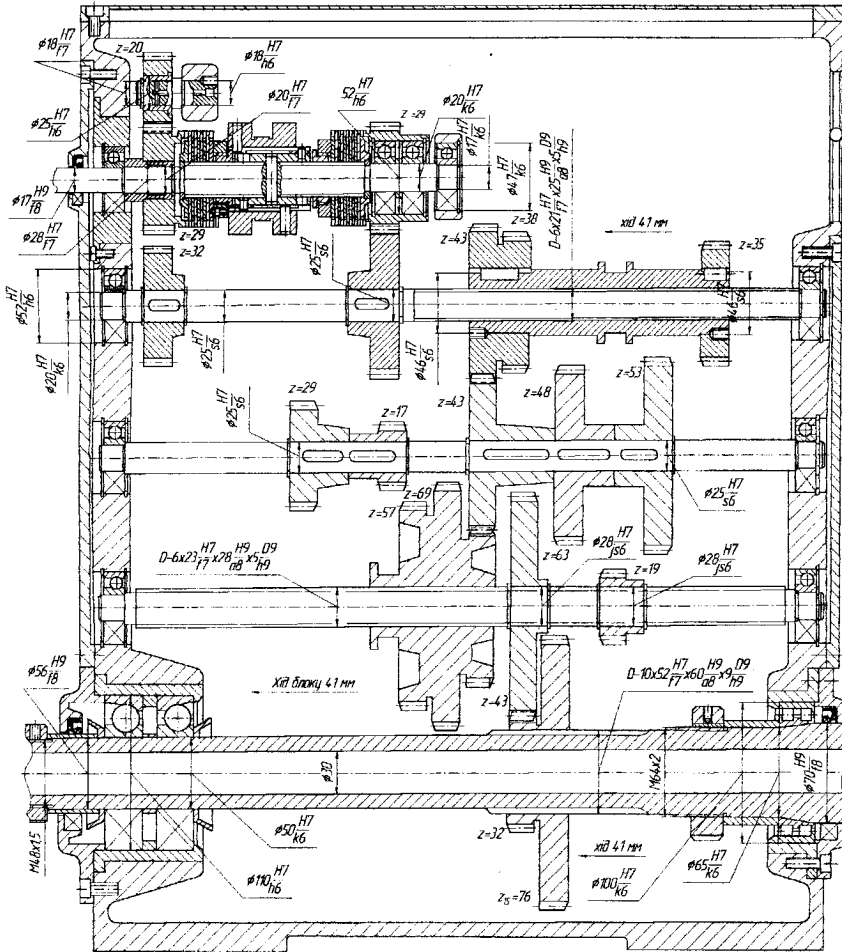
Розгортка поздовжнього перерізу коробки швидкостей верстатів токарної групи
